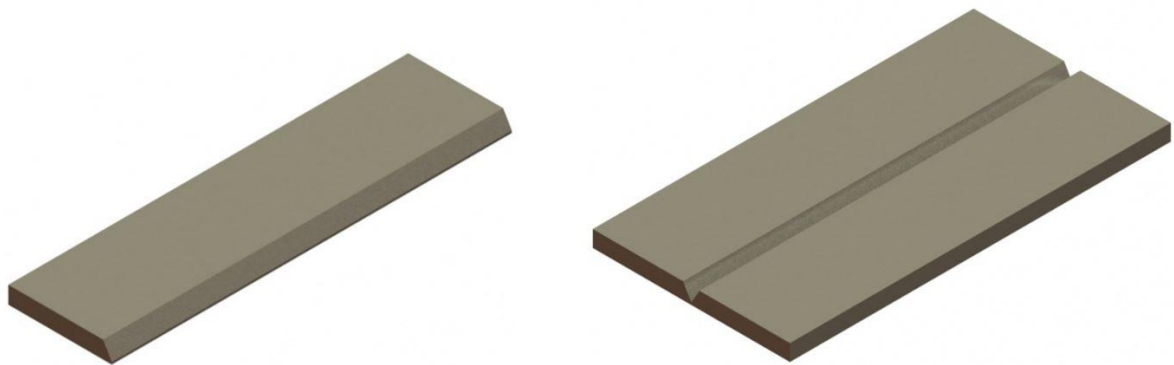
Ilustração do CP e sua montagem na junta a ser soldada
